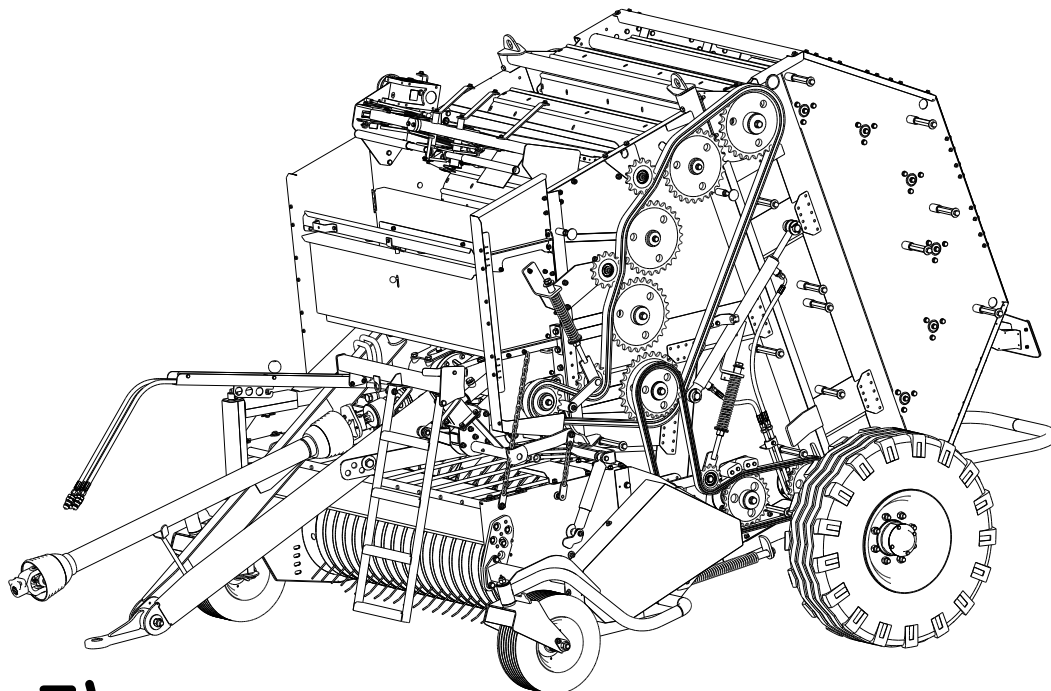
а. Общий вид пресс-подборщика: 1 - корпус передний; 2 - корпус задний; 3 - дышло; 4 - подборщик; 5 - привод пресс-подборщика; 6 - площадка; 7 - режущий механизм шпагата; 8 - механизм обвязки шпагатом; 9 - опора стояночная; 10 - выбрасыватель рулона; 11 - гидросистема; 12 - кронштейны амортизаторов; 13 - электрооборудование; 14 - комплект капотов; 15 - стойка-держатель РВД; 16 - колеса опорные.
